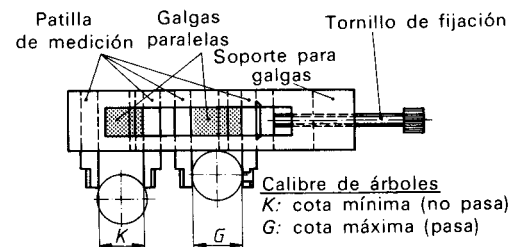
Soporte de galgas usado como calibre de tolerancias.
